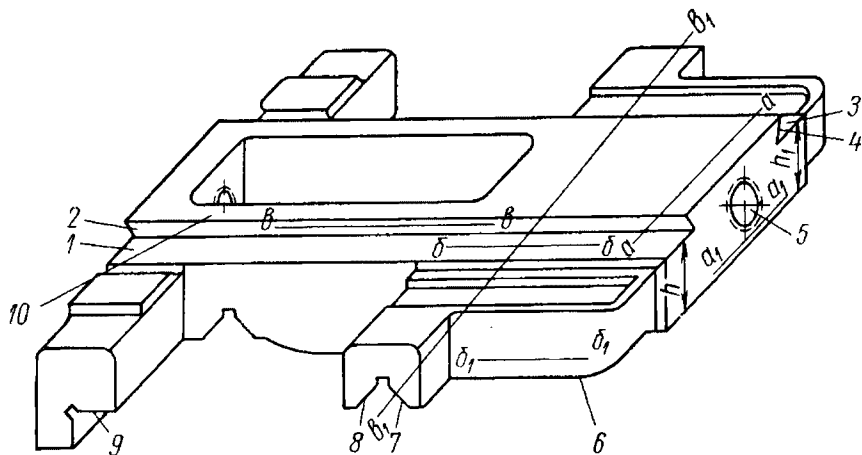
Каретка суппорта токарно-винторезного станка модели 1К62
